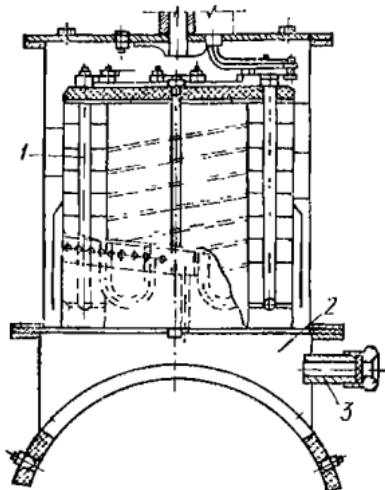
Устройство для местного нагрева труб перед вытяжкой горловины:
